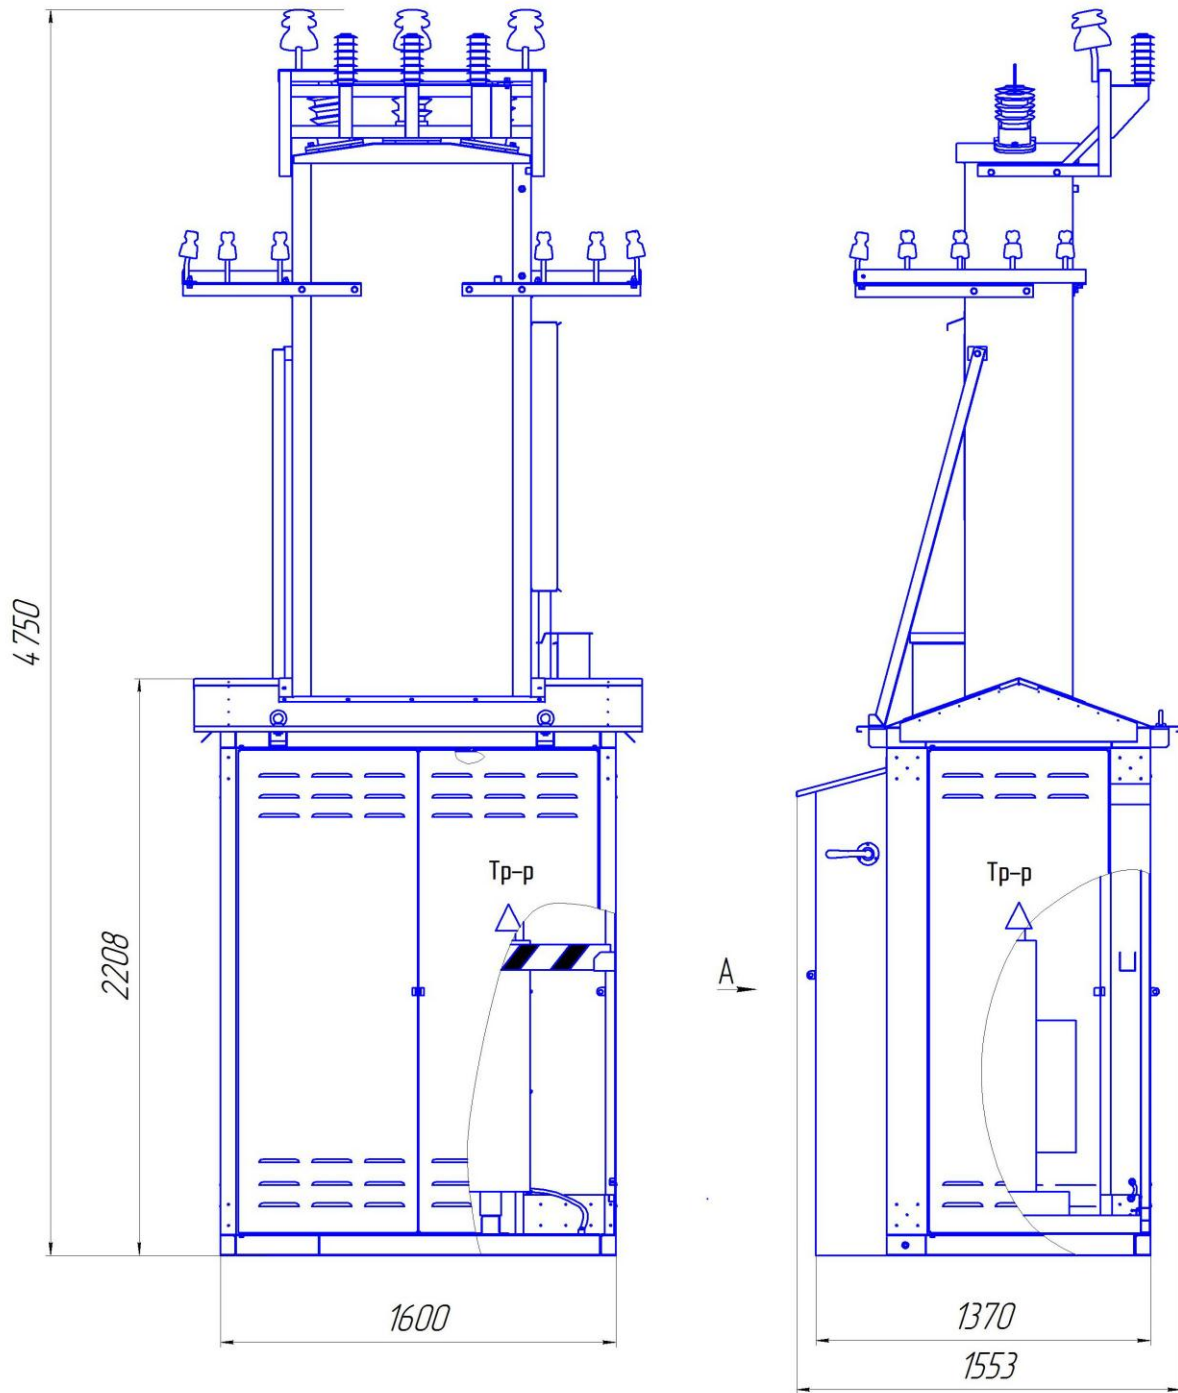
Габаритные и установочные размеры ХКТПН-Орб 07М
